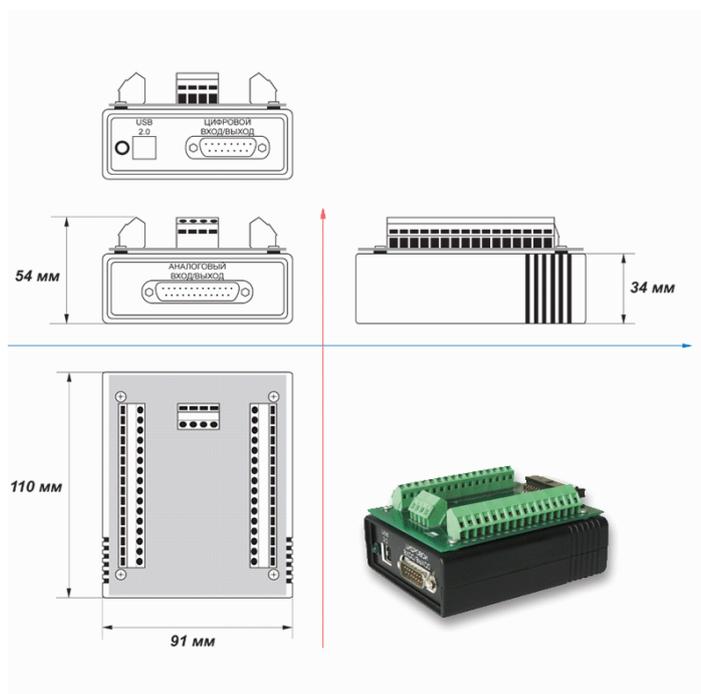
Внешний вид и габаритные размеры модуля ZET
